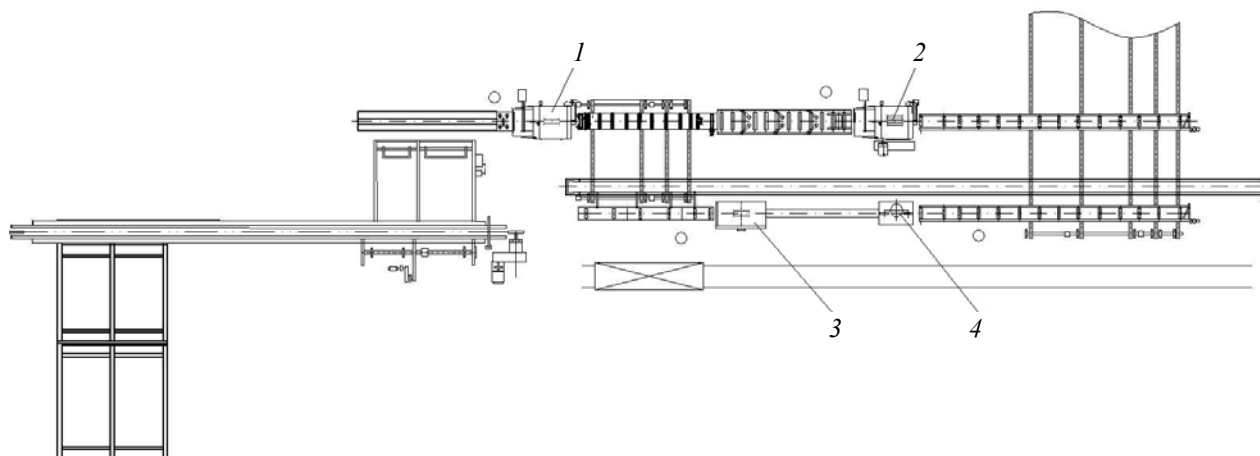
Схема лесопильного потока на базе двухпильного круглопильного станка для распиловки бревен:
